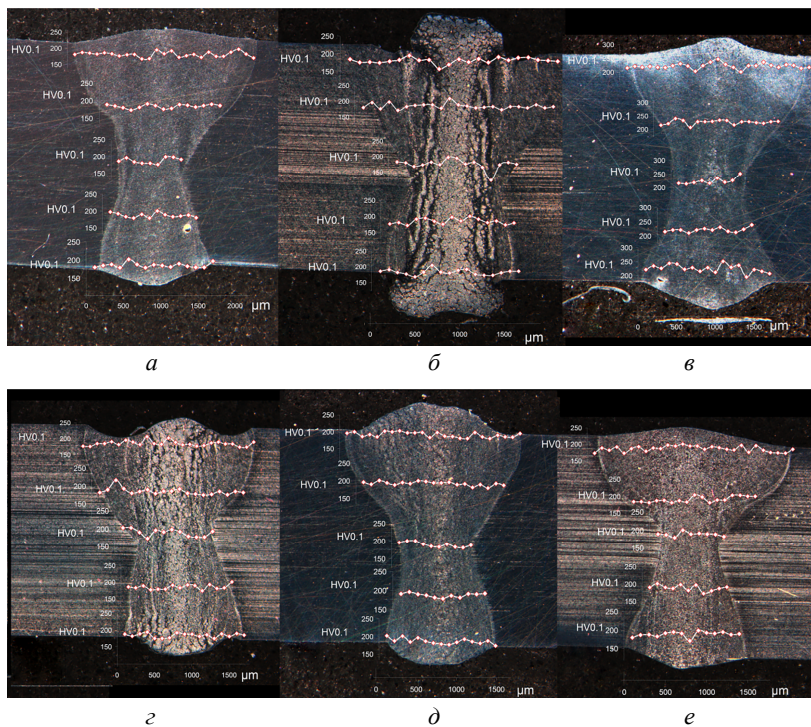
Изображения поперечных сечений сварных соединений и распределение микротвердости на различной глубине сварного шва:
